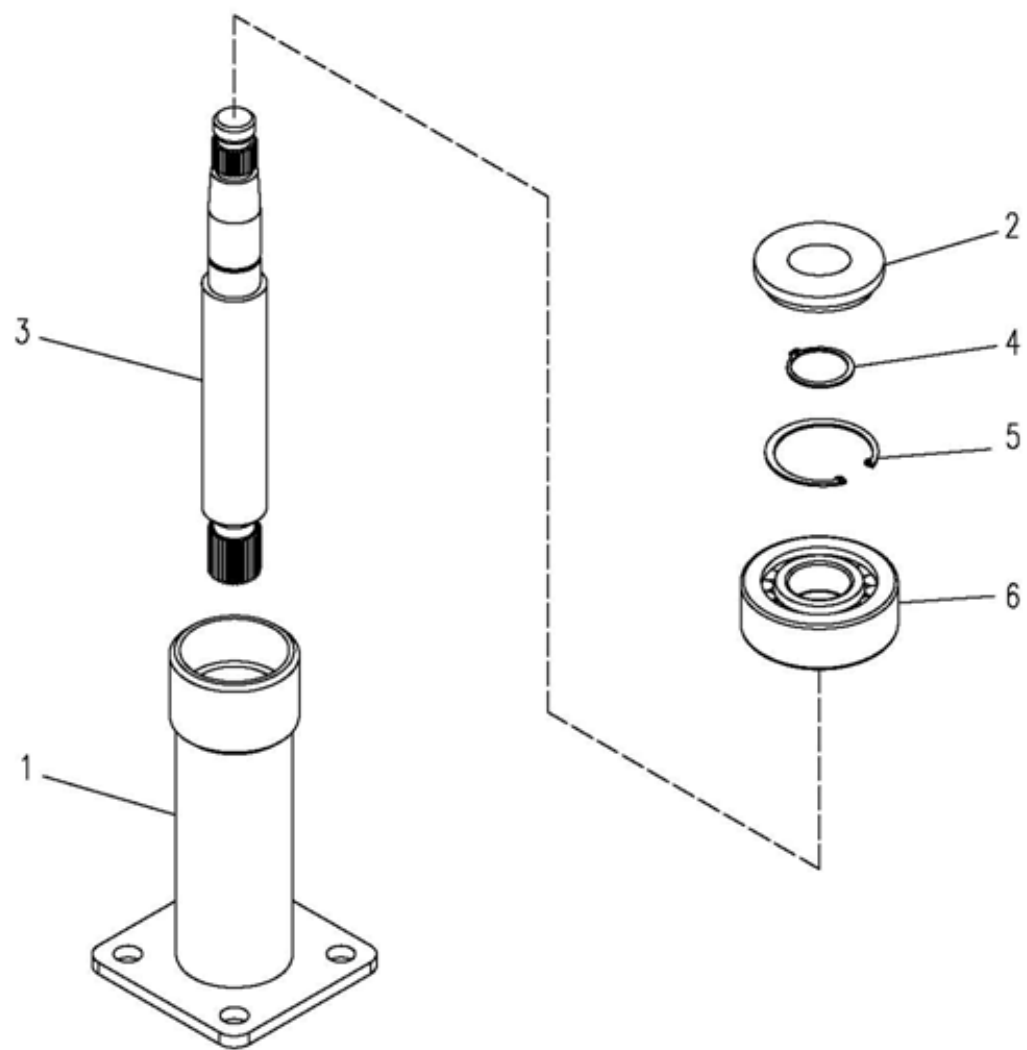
/ Fig.9 / Dib. 9 6222.06.16.000
